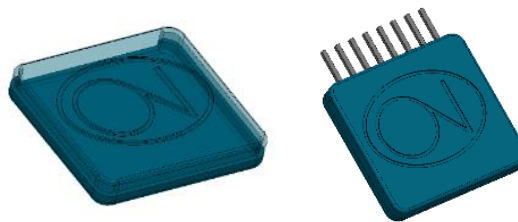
Diseño CAD 3D de envoltorio para placa electrónica WRIST del demostrador SMART ARM PRO
